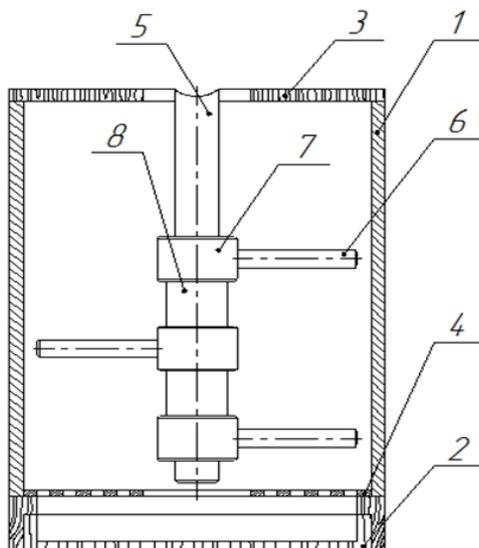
Схема лабораторной установки для очистки перговых гранул от органической оболочки: 1 – рабочая камера; 2 – ящик для сбора гранул; 3 – крышка; 4 – решето; 5 – рабочий вал; 6 – штифт; 7 – втулка фиксации штифта; 8 – распорная втулка
